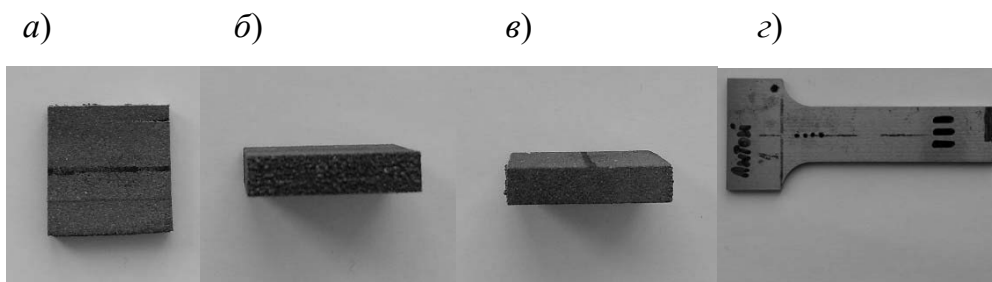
Полученные с помощью СЛС образец-пластина (*а–в*) в форме квадрата (изготовитель 1) и образцы в виде балки (*г*) из стали 09Г2С
